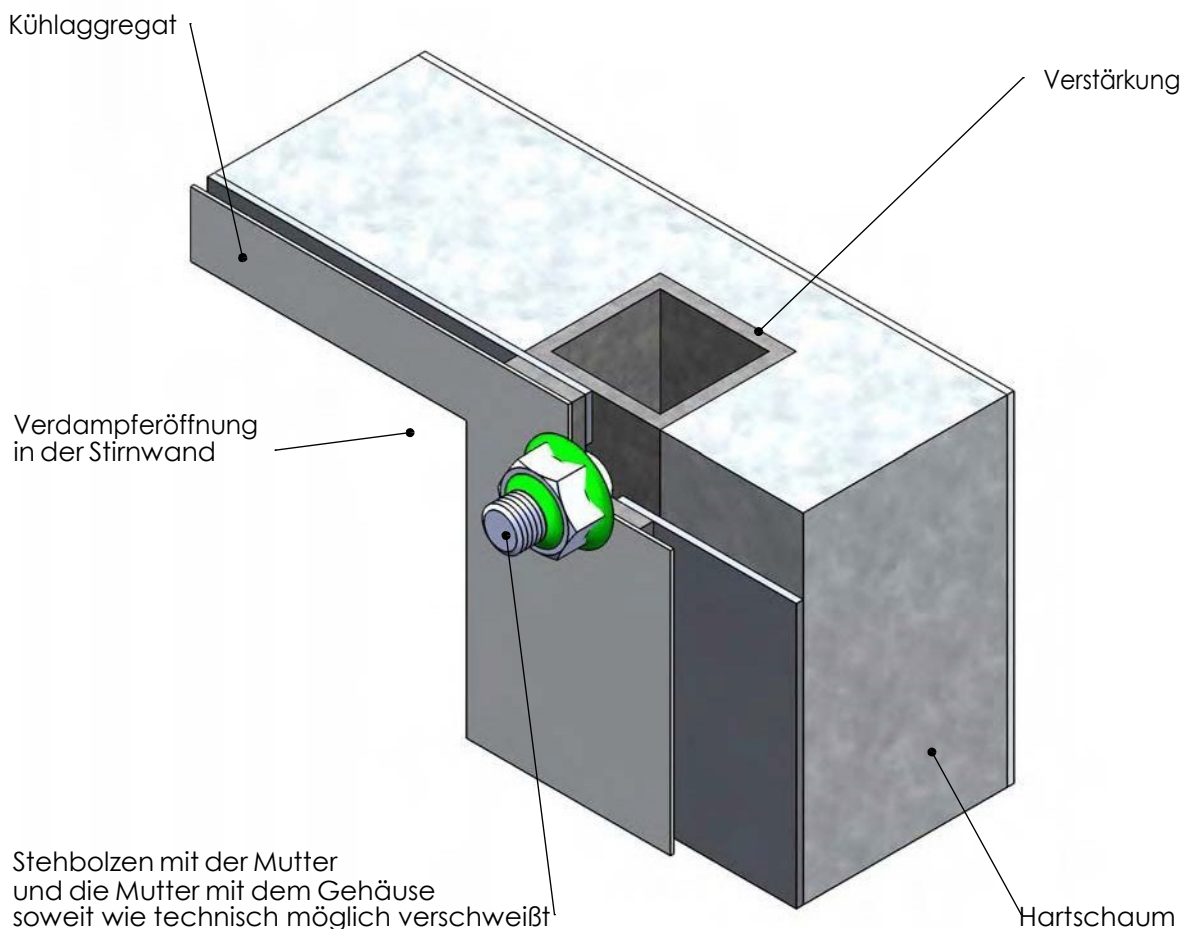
Sicherung mit von innen angebrachten Schrauben
